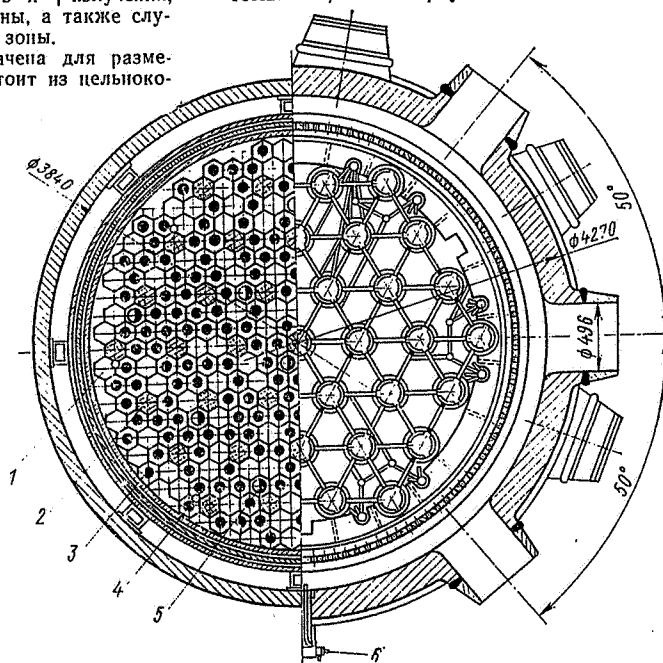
Активная зона реактора ВВЭР-440 (вид сверху):
